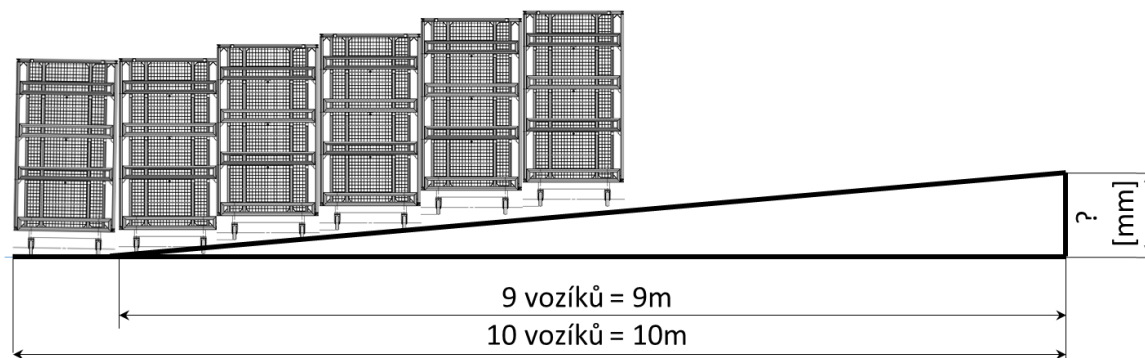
Podrobný konstrukční návrh skladovacího zařízením
